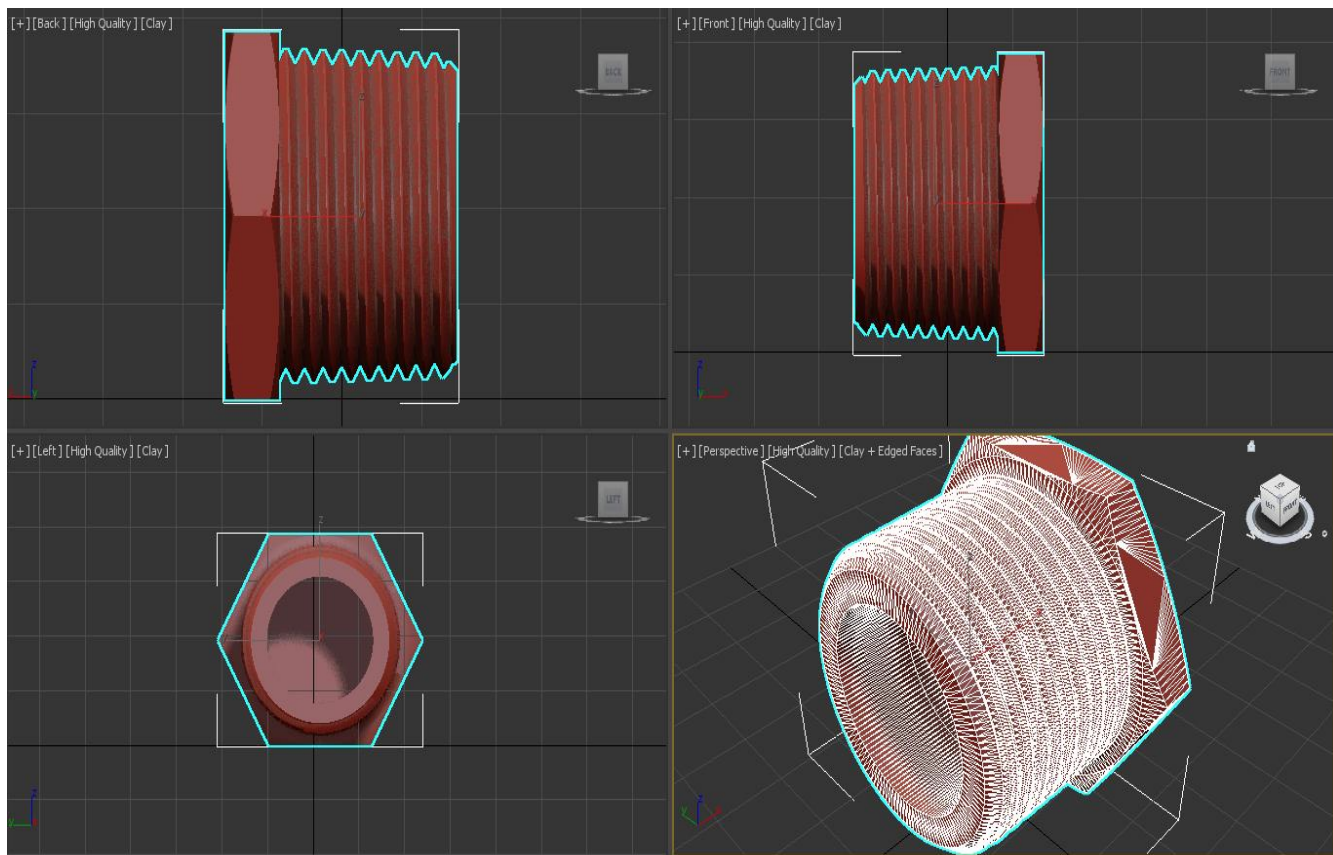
3D-модель дюймовой заглушки для полиэтиленовой трубы
